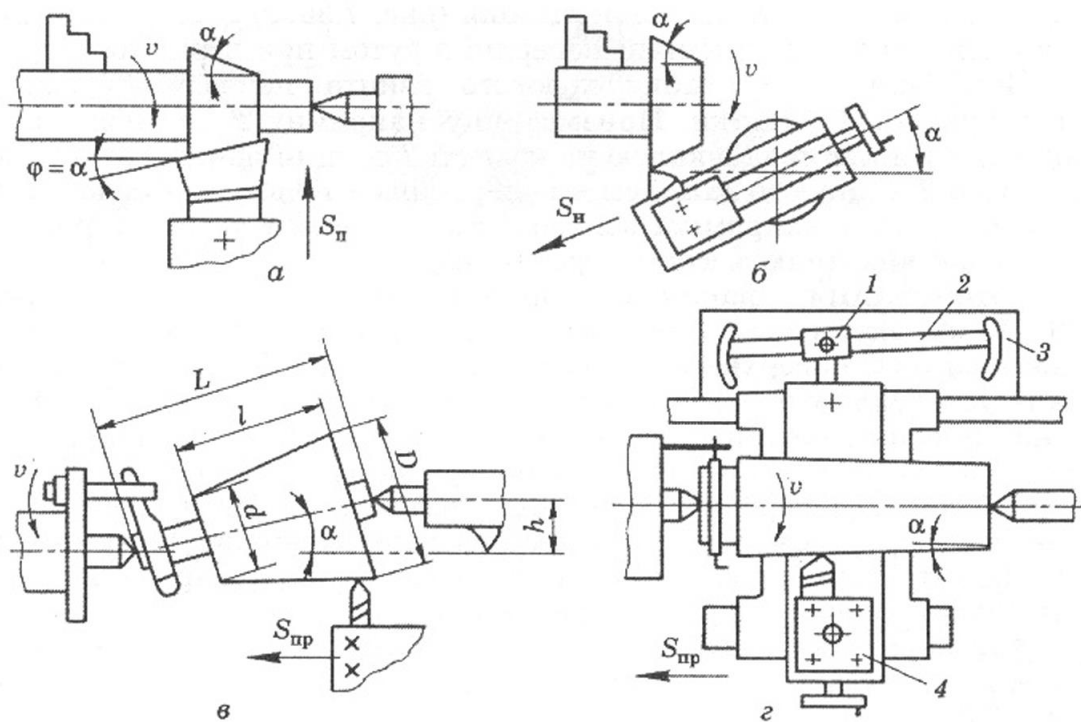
Схеми обробки конічних поверхонь на токарних верстатах
